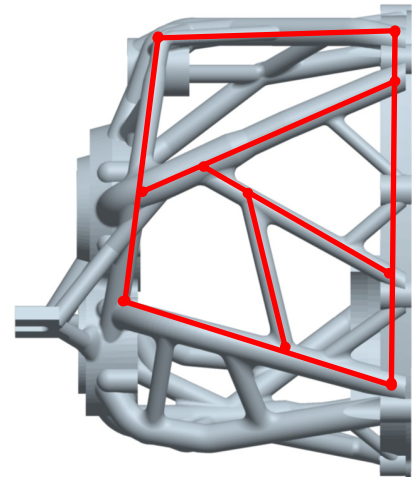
Seitenansicht des Skelettgehäuses
